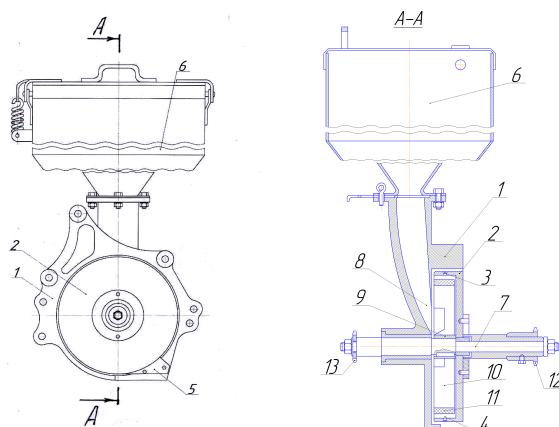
Дозатор насіння сої з внутрішнім заповненням комірок висівного диска насінням: 1 – корпус; 2 – висівний диск; 3 – комірка; 4 – кільцева проточka; 5 – клиновий виштовхувач; 6 – насіннєвий бункер; 7 – вісь; 8 – вхідний отвір; 9 – крильчатка; 10 – лопаті; 11 – еластичні накладки; 12, 13 – приводні зірочки
